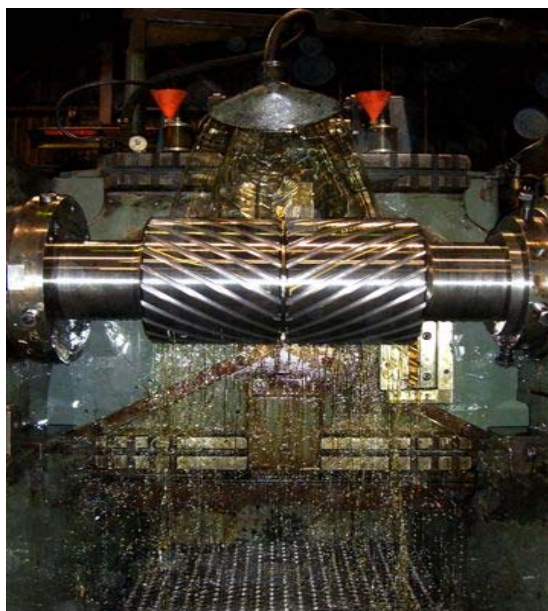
Обработка шевронной вал-шестерни обкаточными резцами
